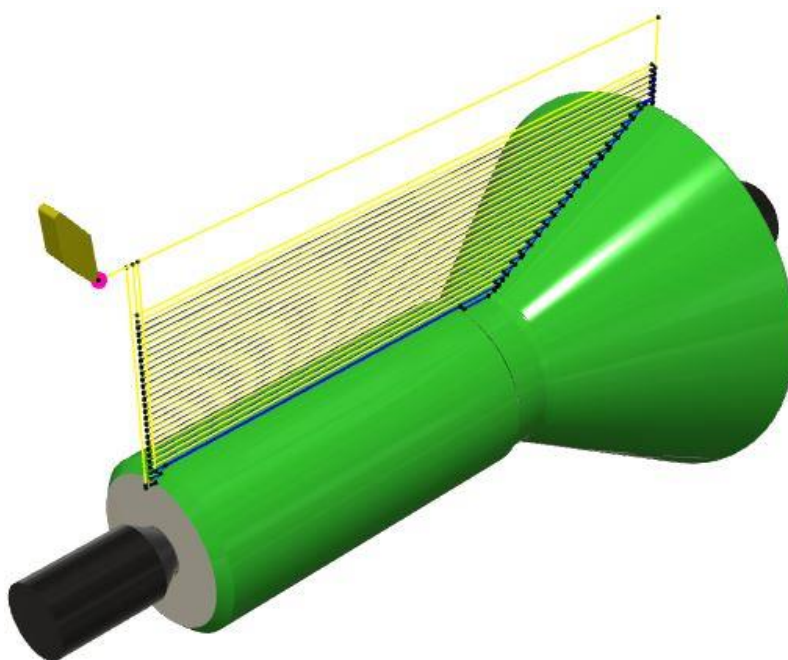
Оброблення зовнішнього контуру фрези
